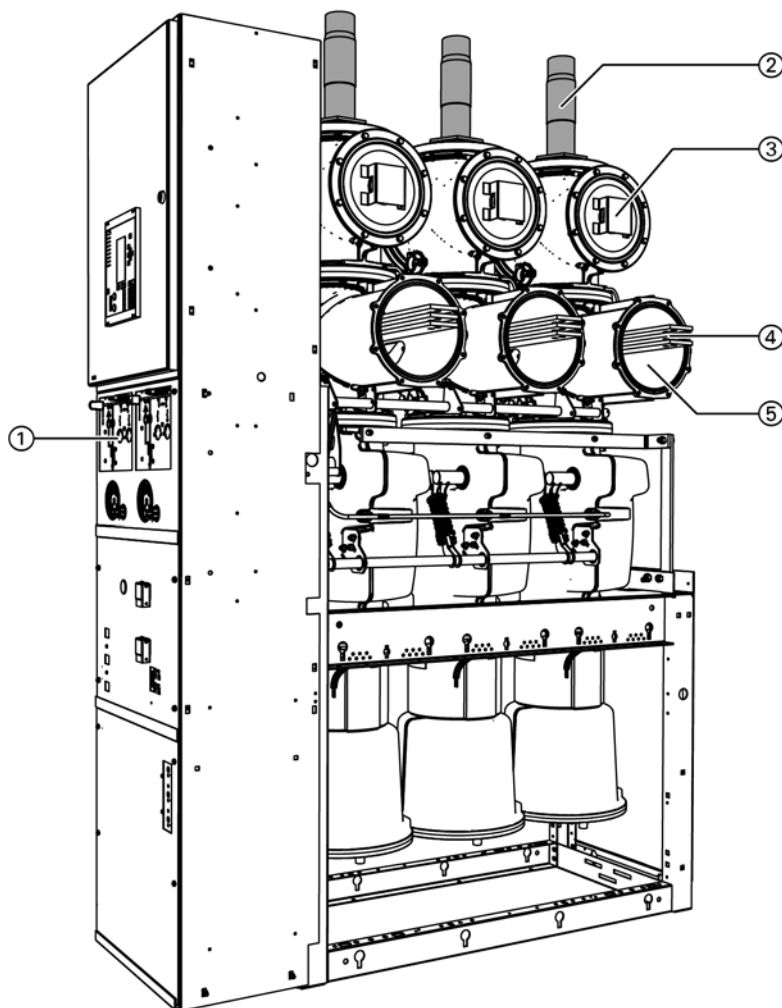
Обзор компоновки сборных шин: шина с изоляцией из твердого диэлектрика с трехпозиционным разъединителем
